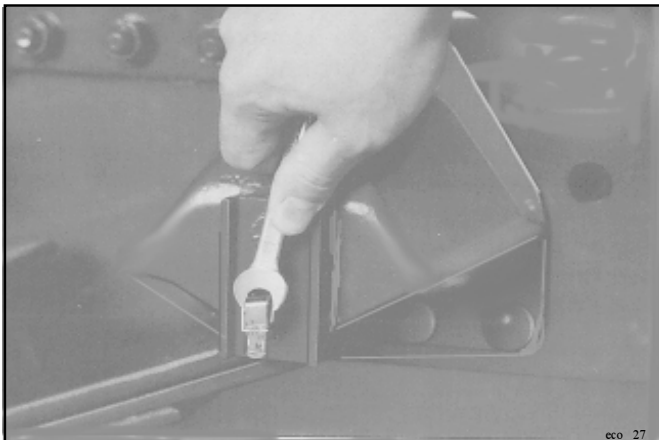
Schmiernippel entfernen und Verschraubung eindrehen
